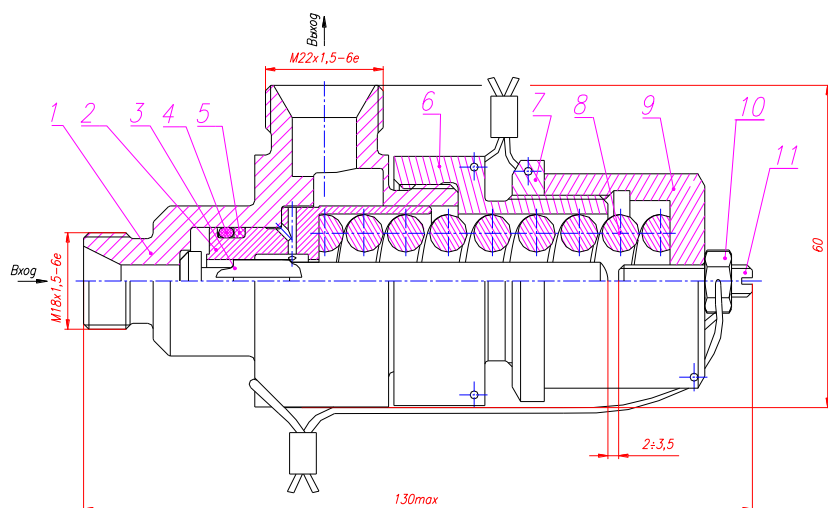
Предохранительный клапан КПП – (50-180): 1-корпус, 2-седло, 3-клапан, 4-кольцо, 5-кольцо, 6-крышка, 7-гайка, 8-пружина, 9-крышка, 10-гайка, 11-винт.
